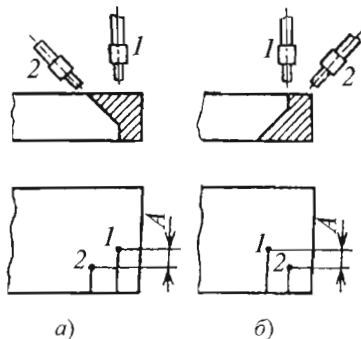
Схемы расположения машинных резаков при одностороннем скосе кромок под сварку:
